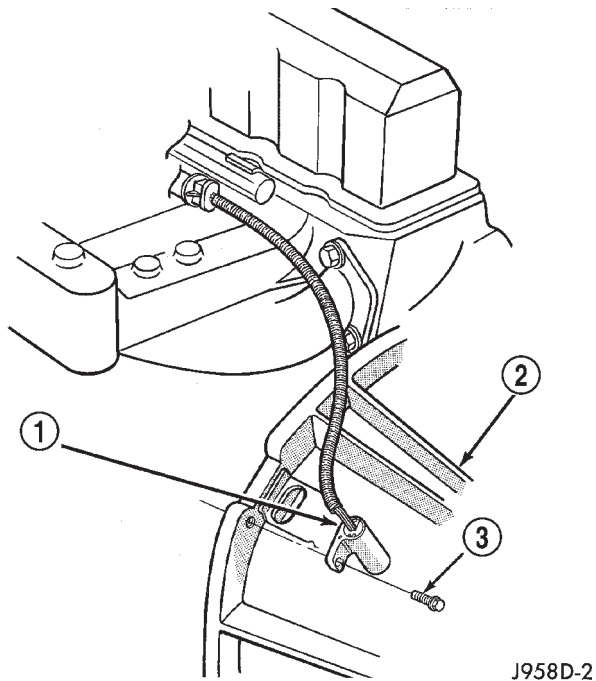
Sensor de posición del cigüeñal - Motor 2.5L
